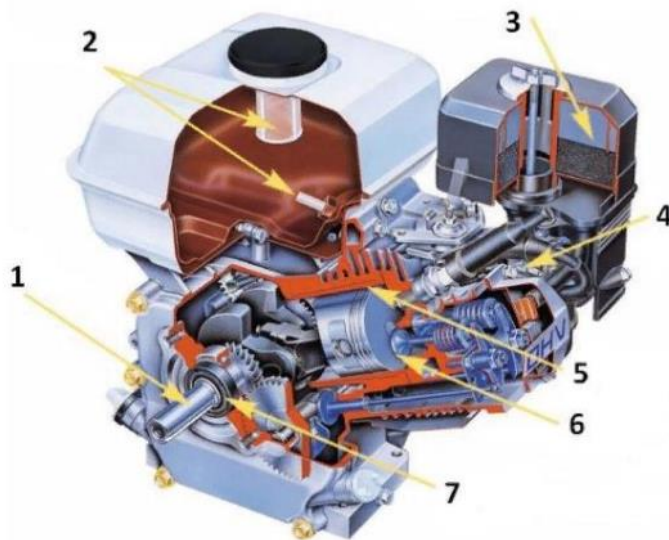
Устройство четырехтактного бензинового двигателя: 1 – кованный коленвал; 2 – топливные фильтры; воздушный фильтр; 4 – электронное зажигание; 5 – цилиндр; 6 – клапана; 7 – опорный подшипник
